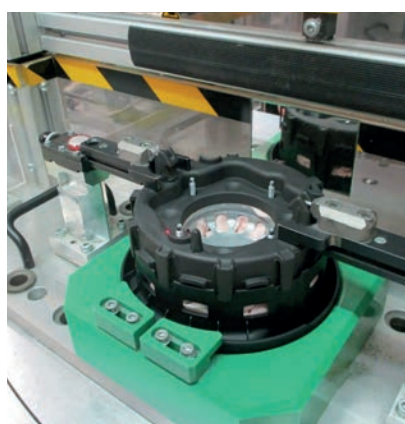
Assemblaggio dell'intero modulo airbag con la parte realizzata in stampa 3D e nel materiale composito Windform® SP. Courtesy Joyson Safety Systems
